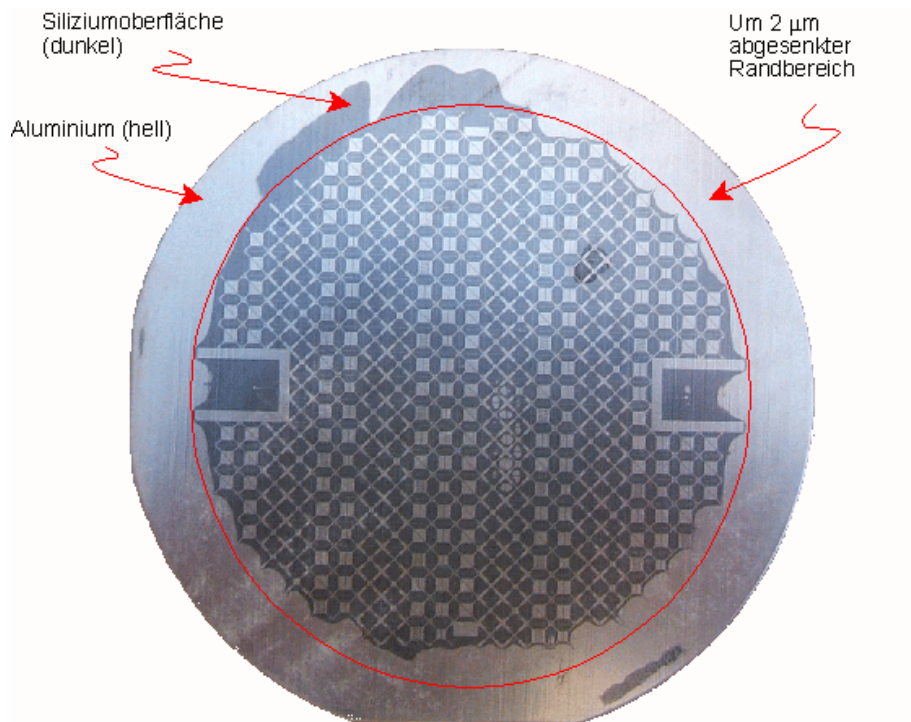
lokal eingätzter und mit Aluminium besputterter Wafer, chemomechanisch poliert. Das Verfahren ist auf die Bearbeitung spröder Schichten ausgelegt; das duktile Aluminium ließ sich nur schwer abtragen.
